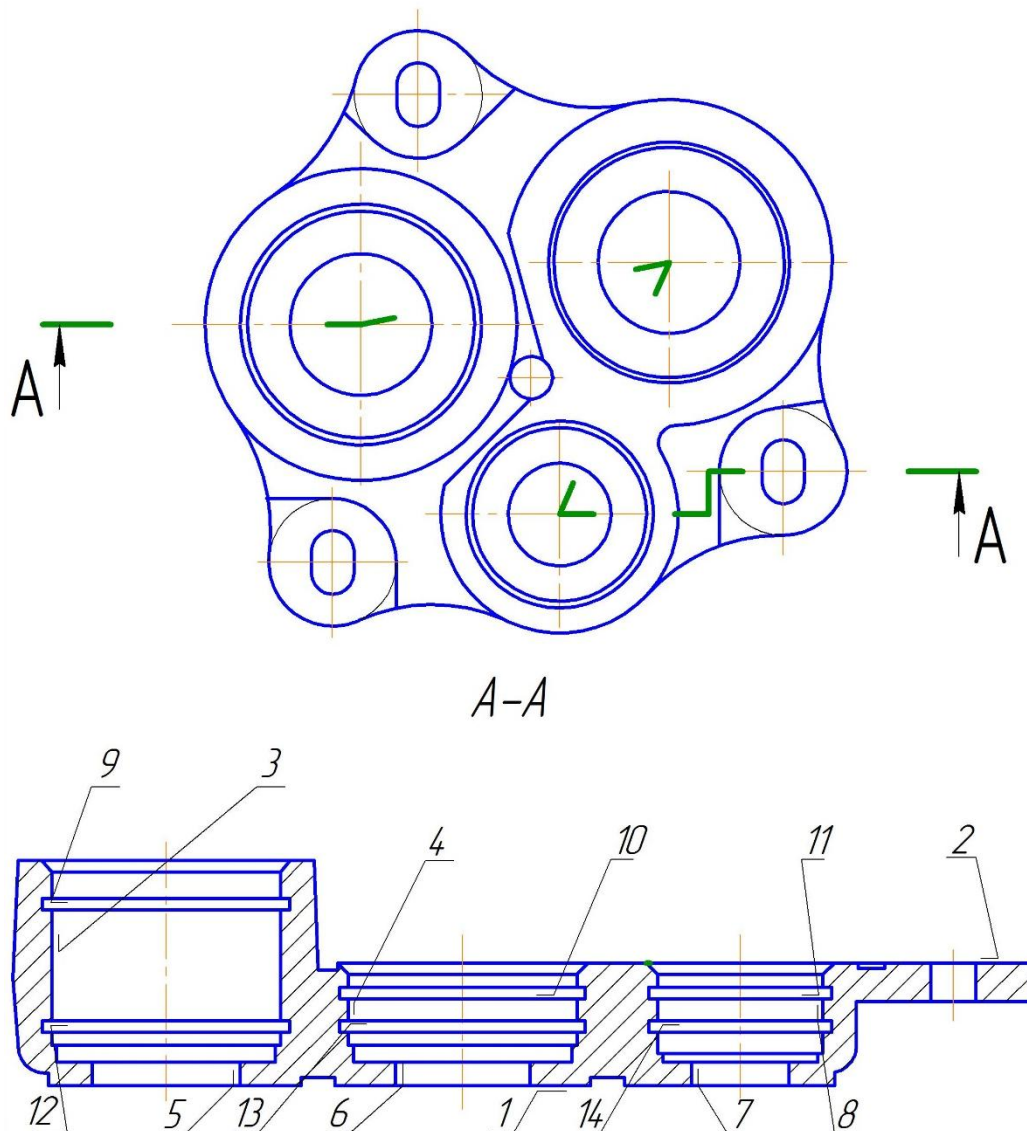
Оброблювані поверхні деталі корпусу
